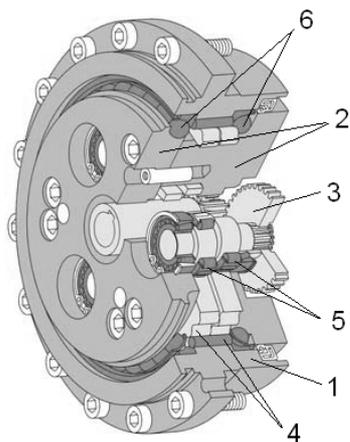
Вариант трехваловой схемы планетарно-цевочного редуктора 2К-V фирмы «Nabtesco»: 1 – корпус; 2 – водило; 3 – эвольвентный сателлит быстроходной ступени; 4 – эпициклоидный сателлит и цевка внецентроидного внутреннего цевочного зацепления; 5 – цилиндрические роликовые подшипники; 6 – шарики радиально-упорных совмещённых опор качения
